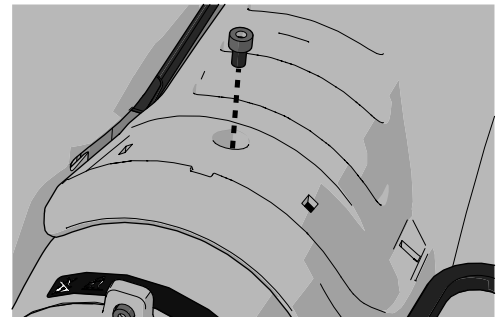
Die Schraube befindet sich in einer Senkbohrung unter der Abdeckung in Akzentfarbe.
